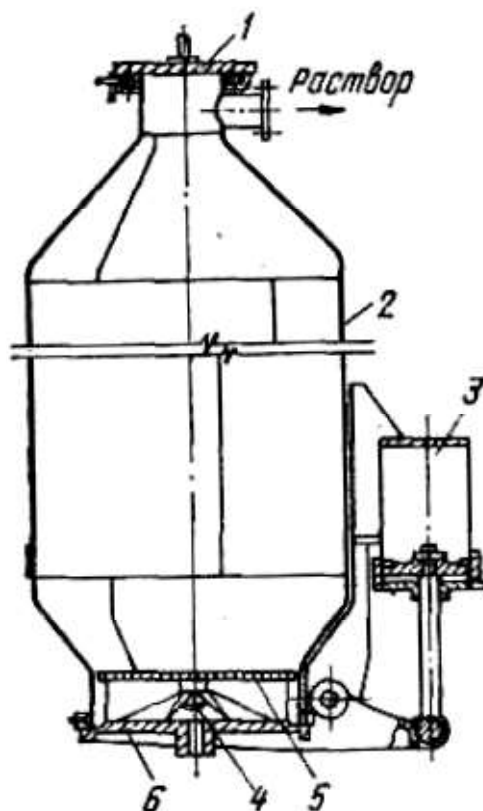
Диффузор для выщелачивания спека: 1 – крышка загрузочного люка; 2 – стальной корпус; 3 – прижимное гидравлическое устройство нижней крышки; 4 – отверстие для подачи растворителя; 5 – решетка откидной крышки; 6 – крышка разгрузочного люка
